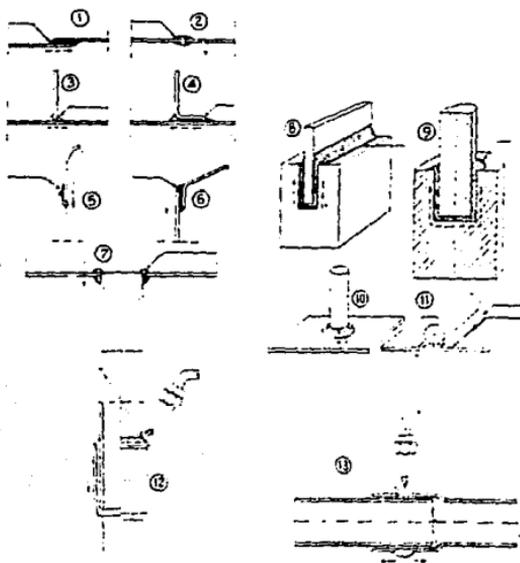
Diversos tipos de juntas realizables por soldadura-braseado.
